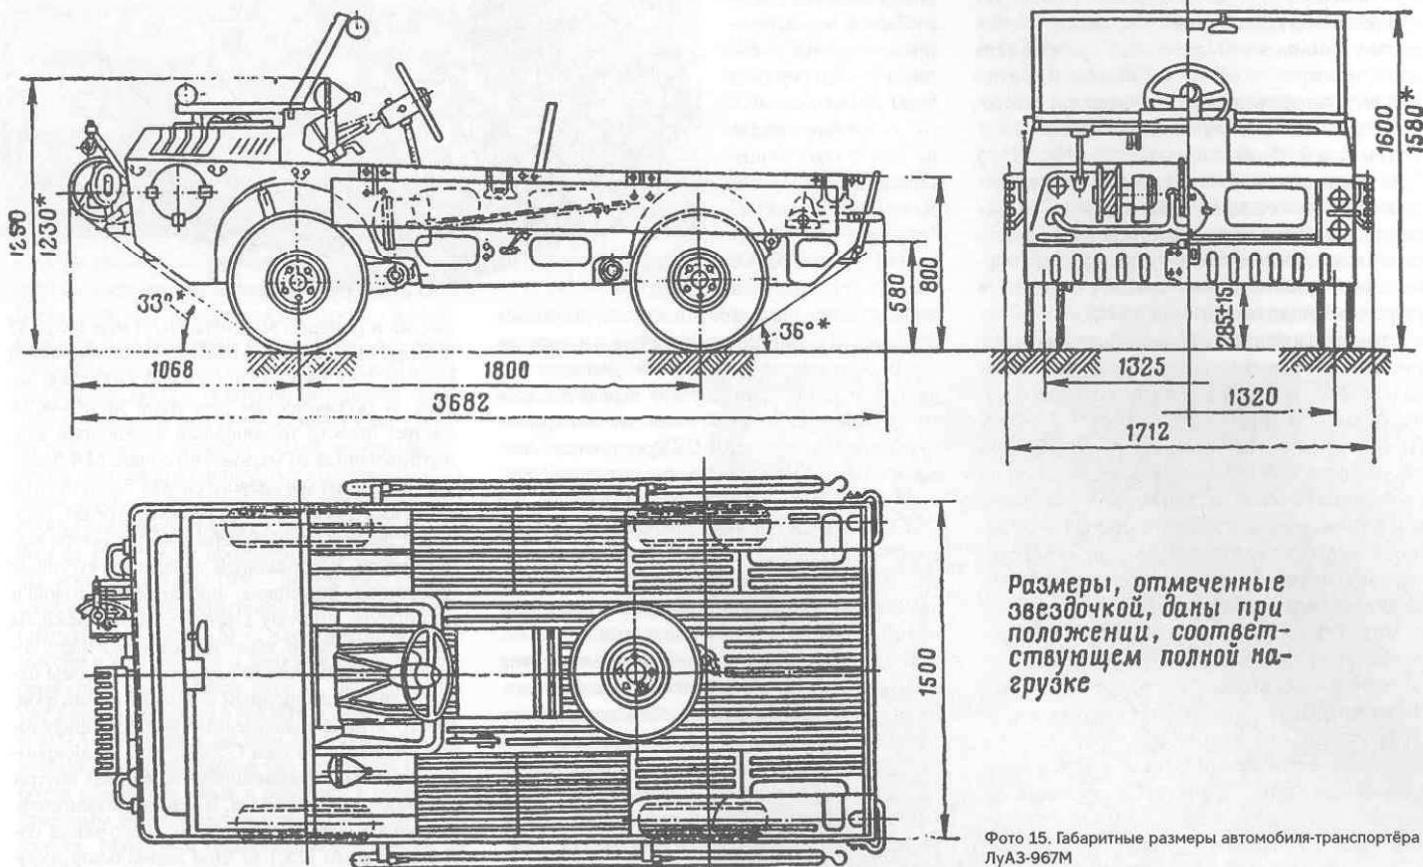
Габаритные размеры автомобиля-транспортера ЛуАЗ-967М
